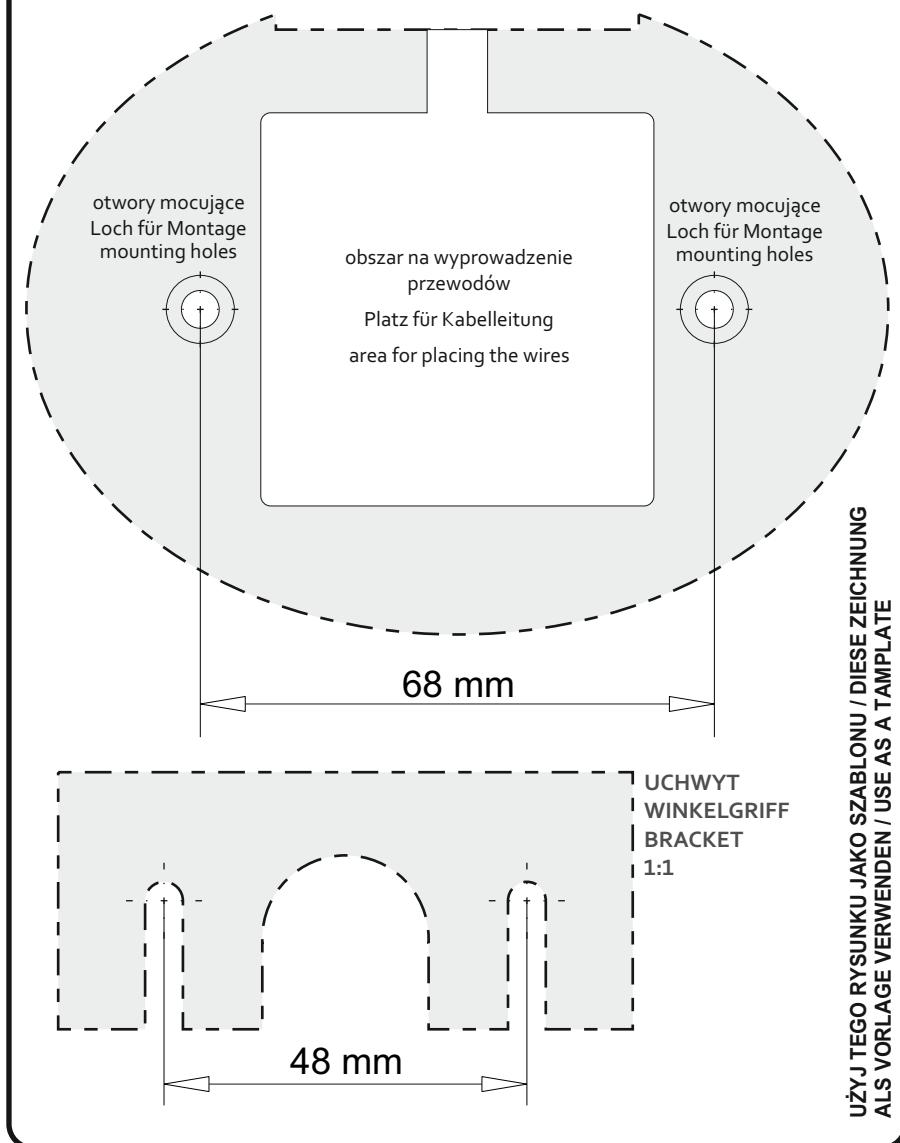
Montaż lampy do powierzchni pionowej za pośrednictwem uchwytu kątowego.
